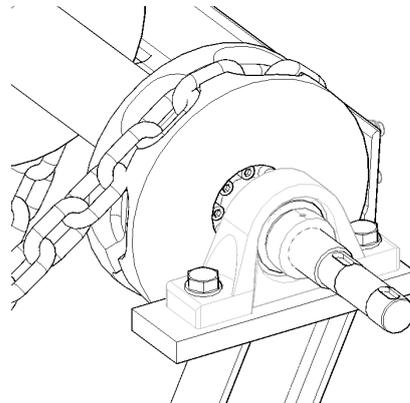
Disposición del soporte de rodamientos en el elevador. Fuente: elaboración propia.
